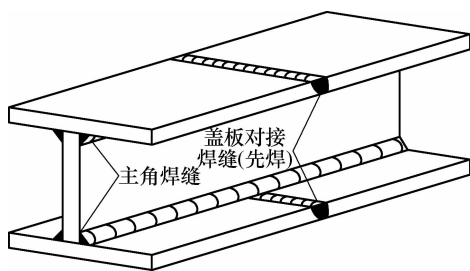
工字梁盖板对接焊缝和主角焊缝的焊接顺序
